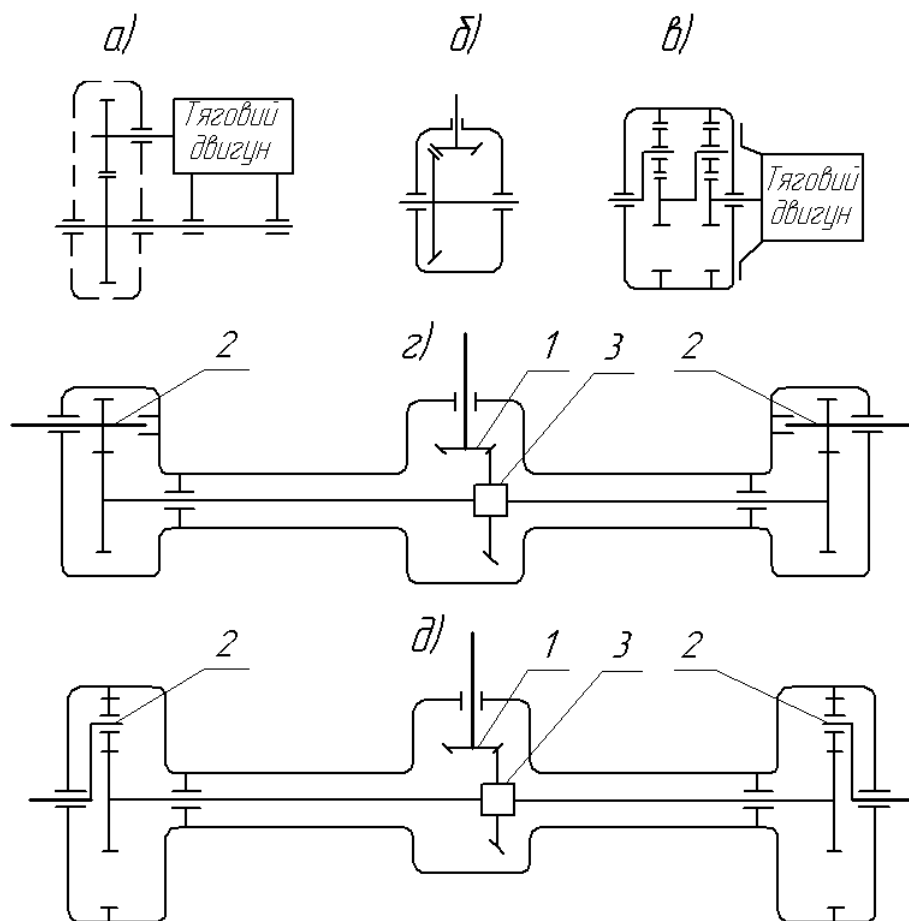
Головні схеми розташування редукторів тягових передач:
